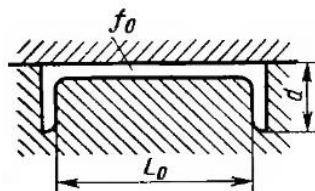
Схема затруднения свободной линейной усадки отливки литейной формой [21]
